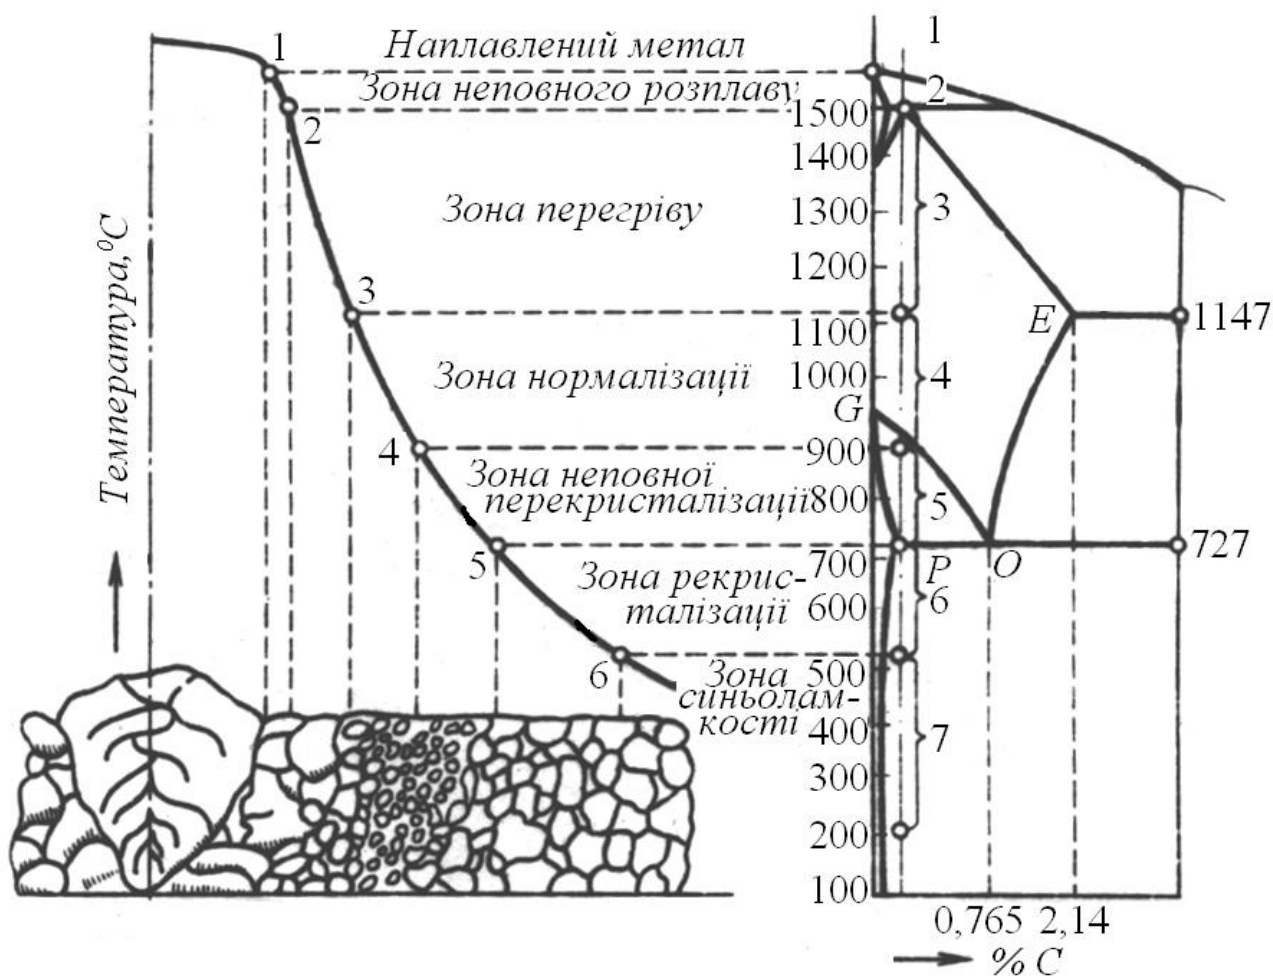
Схема утворення структури зварного шва для низьковуглецевої сталі
